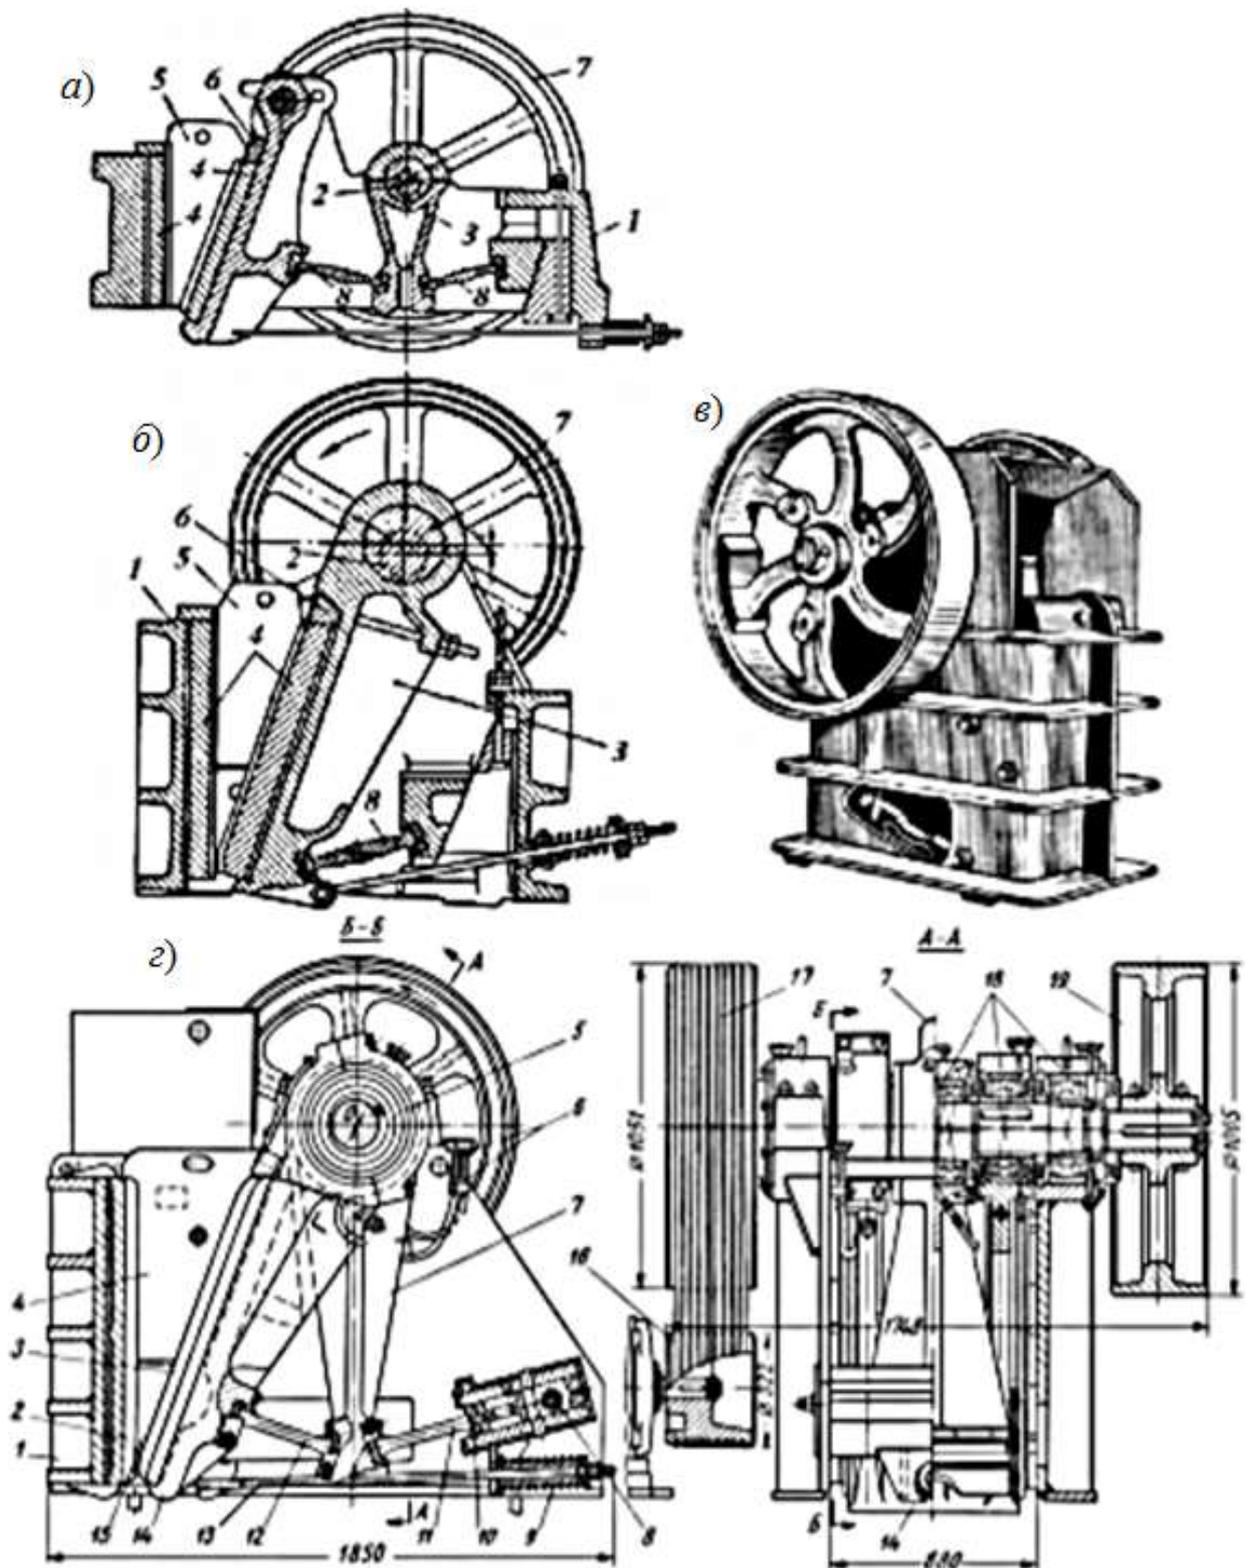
Щековые дробилки: *а* – схема дробилки с простым движением щеки; *б, в* – схема и общий вид дробилки со сложным движением щеки; *г* – схема дробилки с комбинированным движением щеки: 1 – станина; 2 – неподвижная дробящая плита; 3 – подвижная дробящая плита; 4 – верхняя футеровка; 5 – эксцентриковый вал; 6 – маслоуказатель; 7 – шатун; 8 – механизм регулирования выходной щели; 9 – пружина
